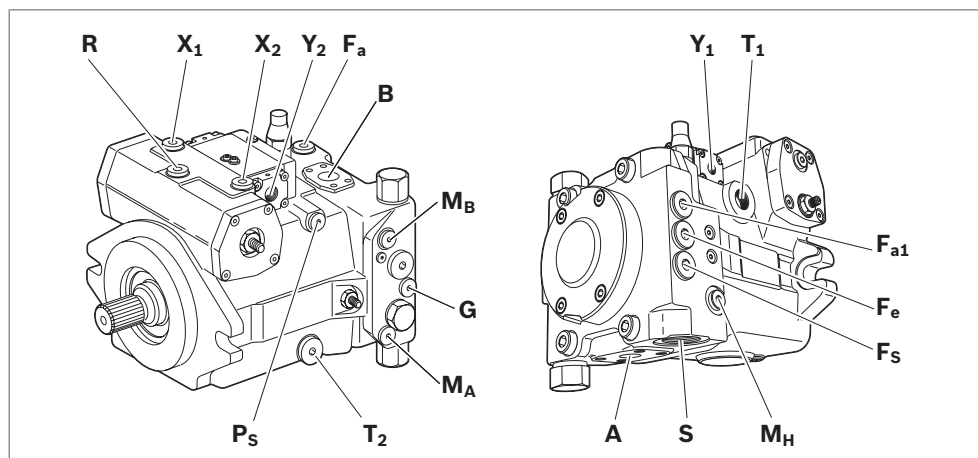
Обзор присоединений A4VG, номинальный размер 40, 56
